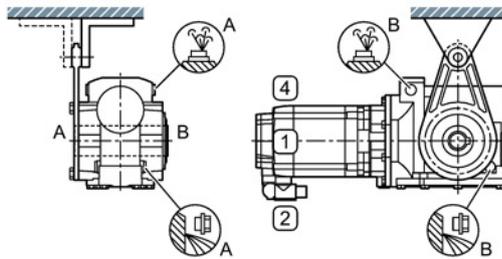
Einbautagen für Stirnradschneckengetriebe CAD, Aufsteckausführung, Baugröße 29, 2-stufig
